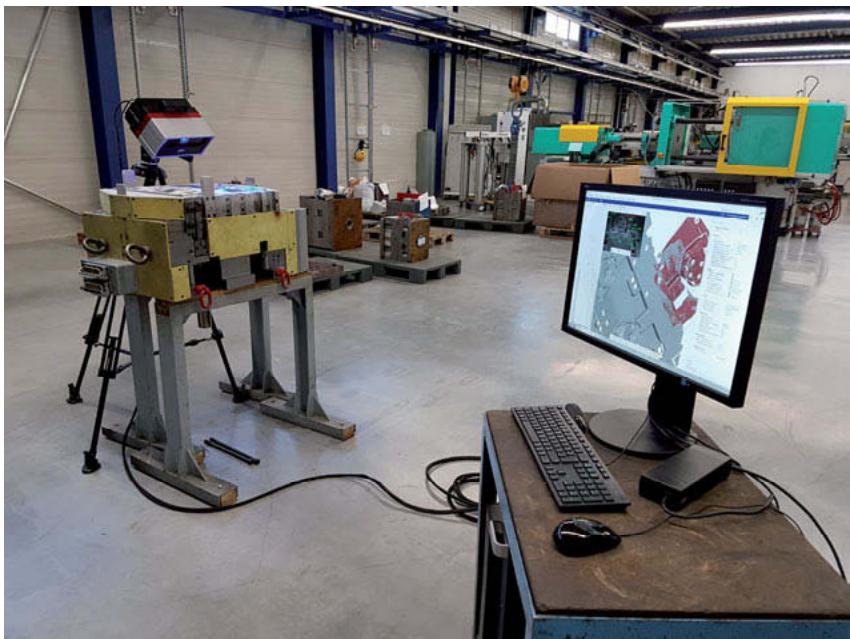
Werkzeugvermessung mit dem Streifenlicht vor Ort [Quelle: LKT]
